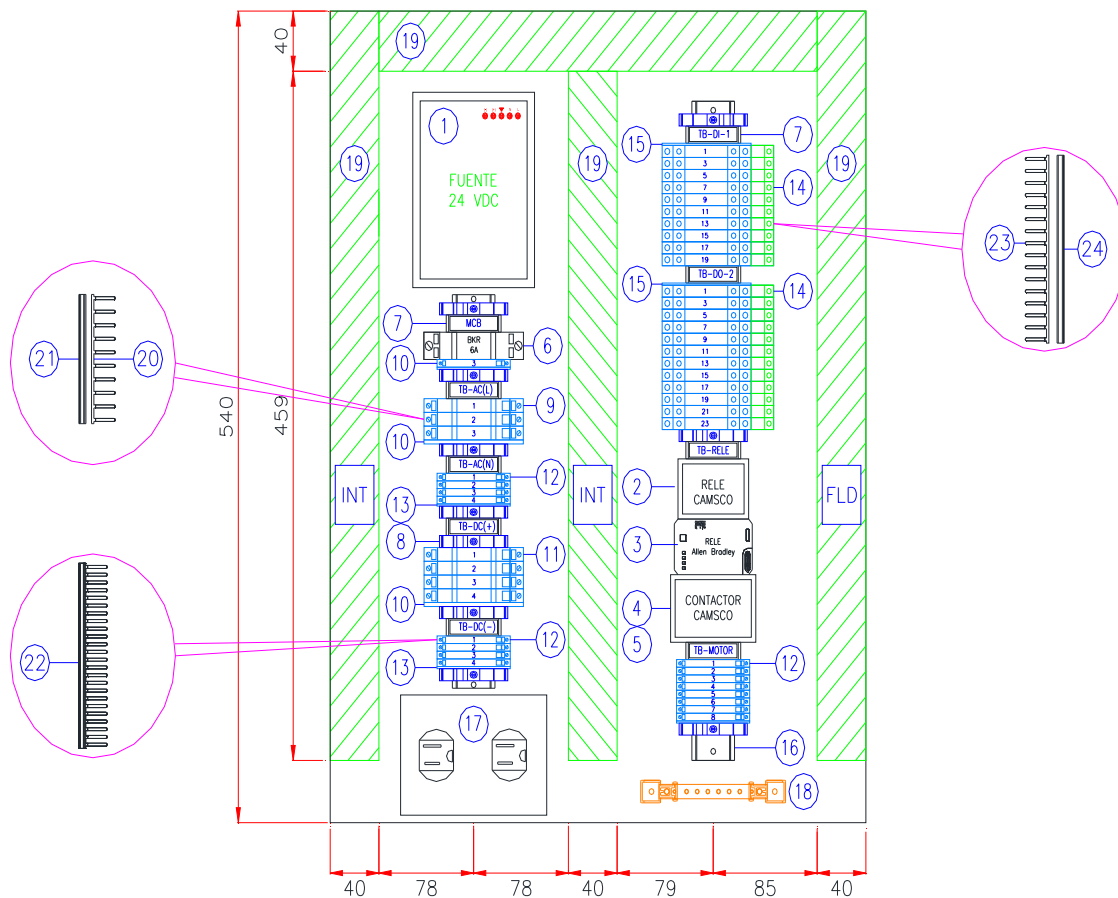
Layout del tablero de control (Fuente: Autor)
